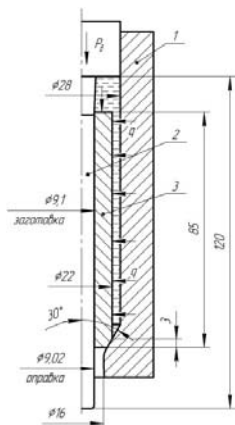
Расчётная схема гидропрессования трубчатых заготовок на оправке
